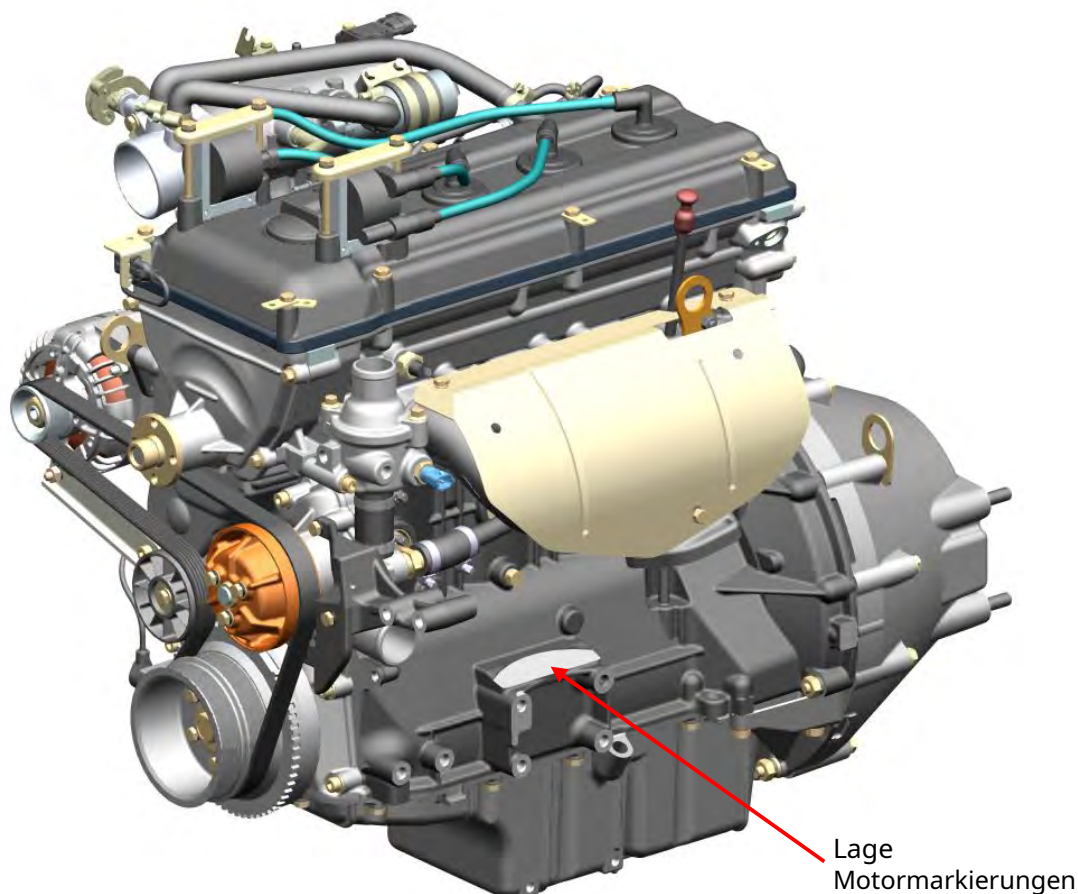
Gesamtansicht des Motors mit Halterung der Servolenkungspumpe
